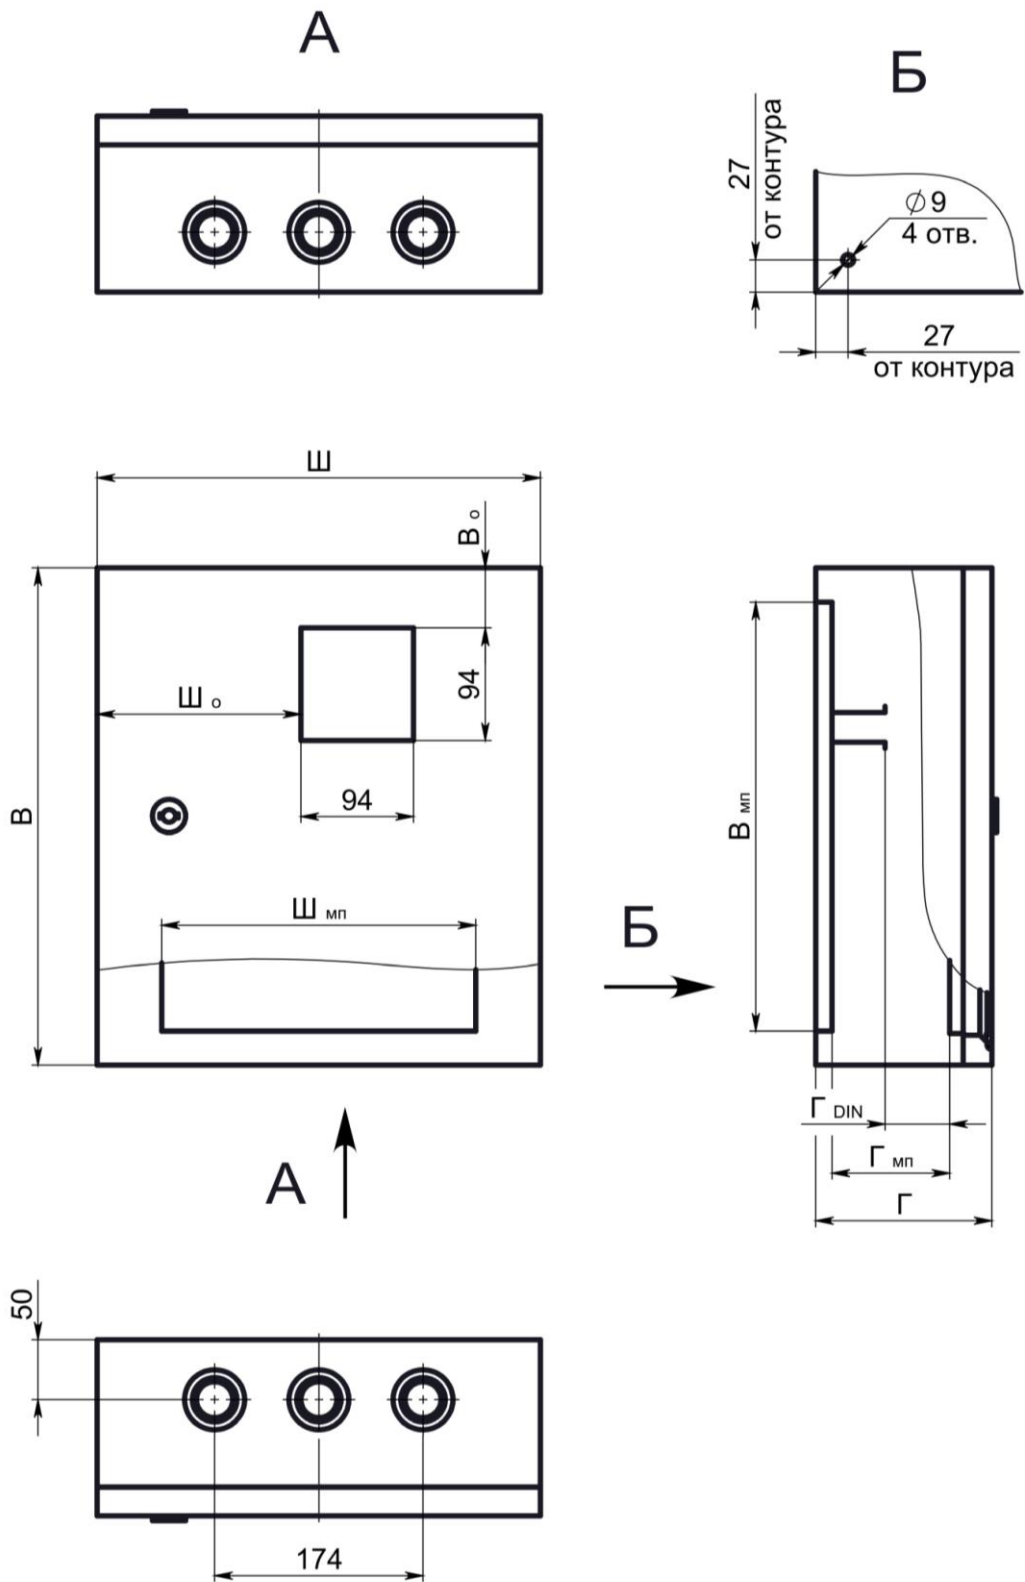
Габаритные, установочные и присоединительные размеры корпуса ЩУРН-ПРО-3-МП/8-415x370x147-IP66-УХЛ1 (код 367475)
